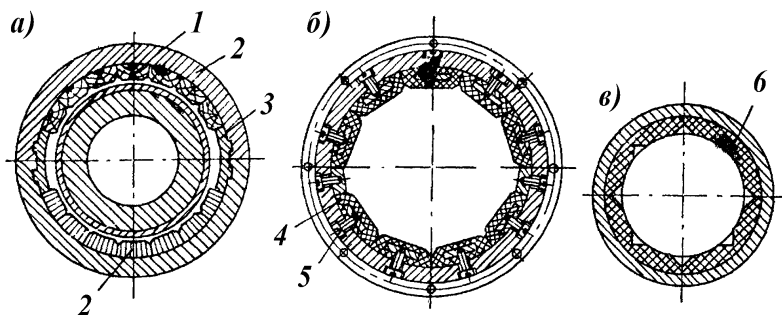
Конструкция дейдвудных подшипников: *а* – с бакаутом или ДСП, *б* – резино-металлический наборный, *в* – резиновый литой; 1 – бруски бакаута или ДСП, 2 – дейдвудная втулка, 3 – вставки, 4 – резино-металлические планки, 5 – винты, 6 – литая резина с углублениями
